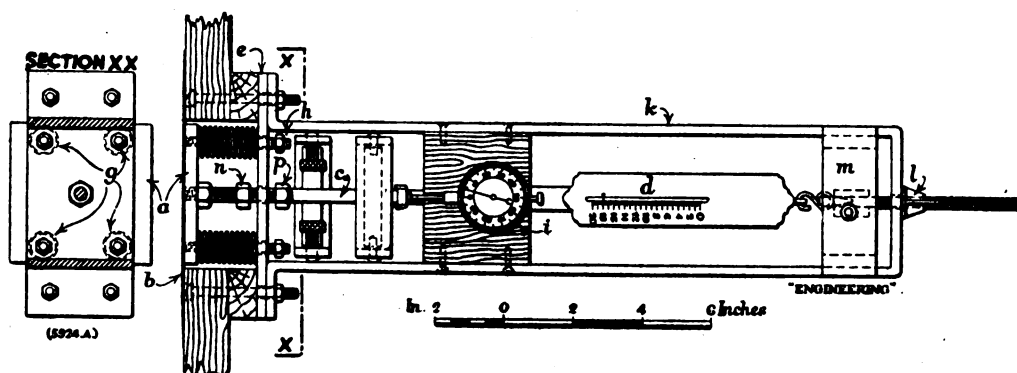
e 3. — Apparecchio per la misura della pressione laterale su una parete: sezione e vista dall'alto.
